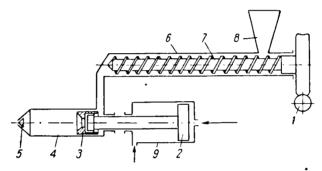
Схема литьевой машины с червячным предпластикатором:
